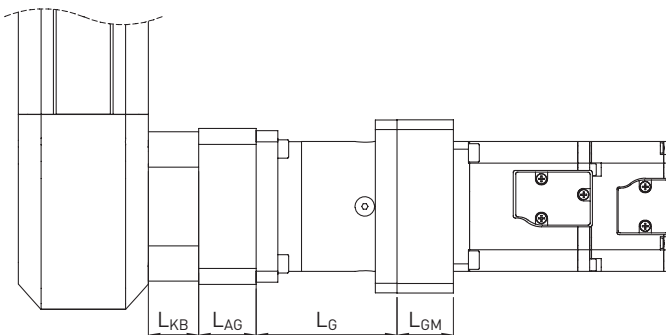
Motoranbindung Linearmodul HM-B mit Getriebe
